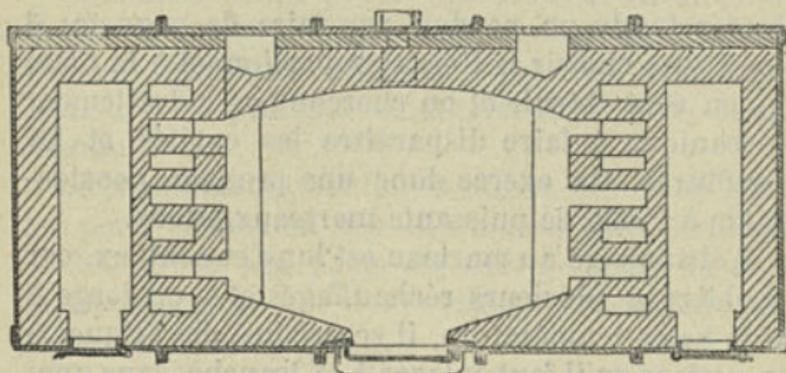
Four à souder et à chauffer, système Siemens (coupe horizontale).
